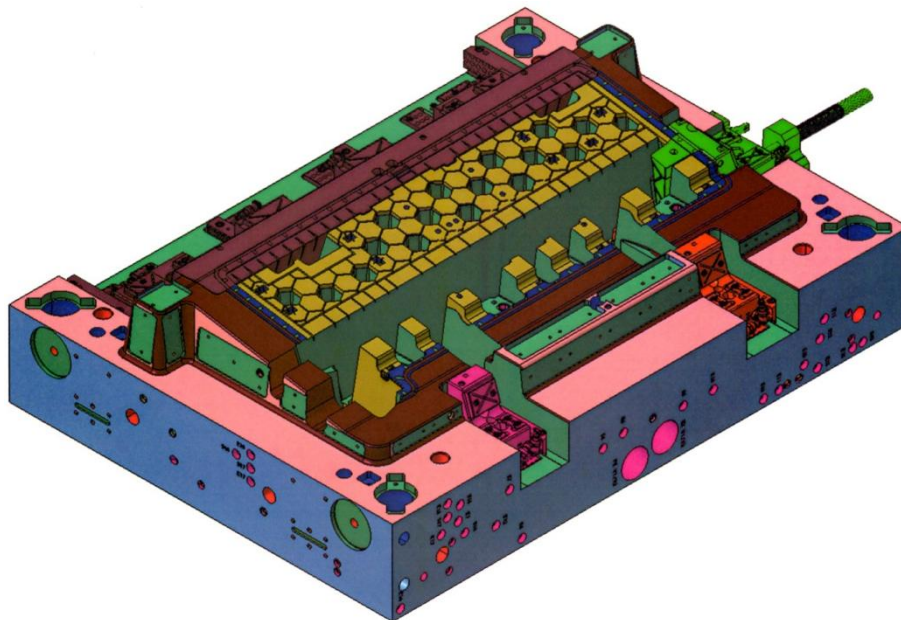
Conjunto placa-macho e movimentos mecânicos.
